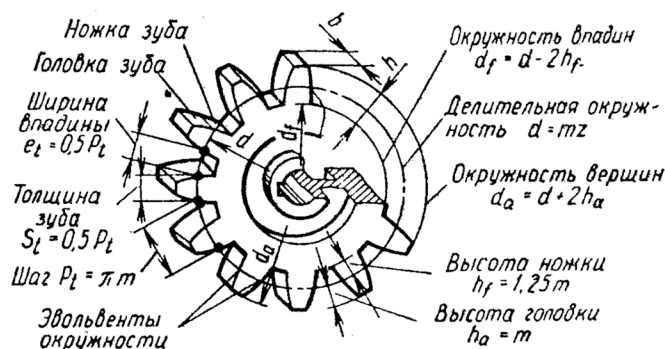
Основные размеры зубчатого колеса и передачи
